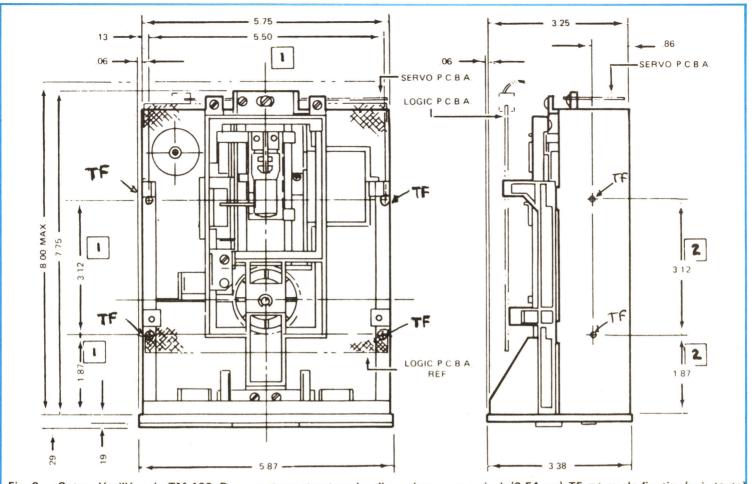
Cotes détaillées du TM 100. Document constructeur, les dimensions sont en inch (2,54 cm). TF = trou de fixation (voir texte)
